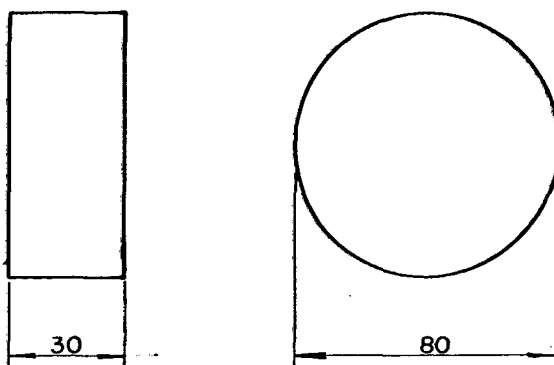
Dimensões do corpo de prova utilizado nos ensaios de furação em cheio e com pré-furo.
